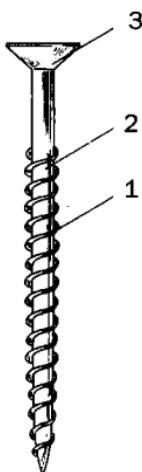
Общий вид шурупа с двухзаходной резьбой: 1 — резьба; 2 — тело; 3 — головка
